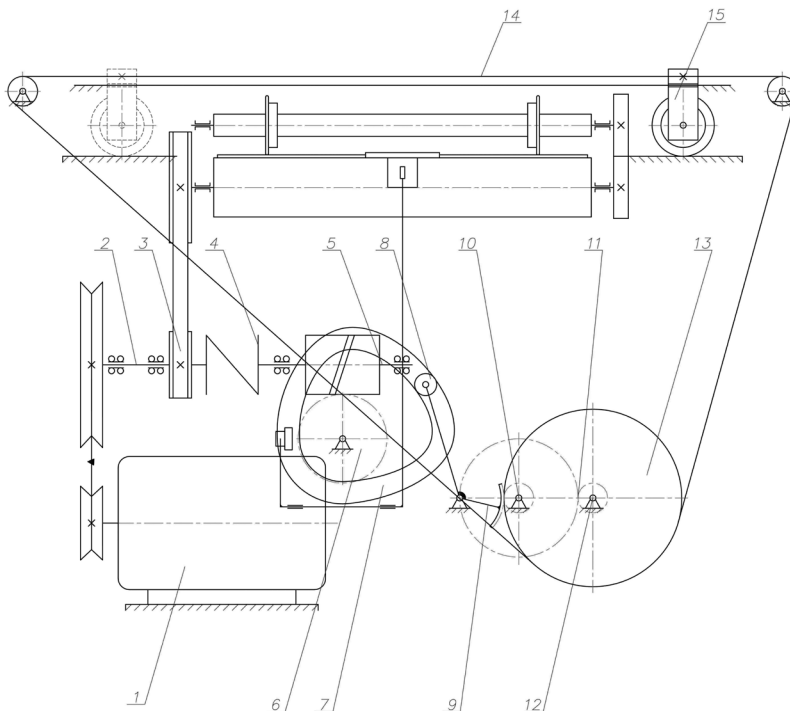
Кінематична схема привода двосекційного бігувального верстата
